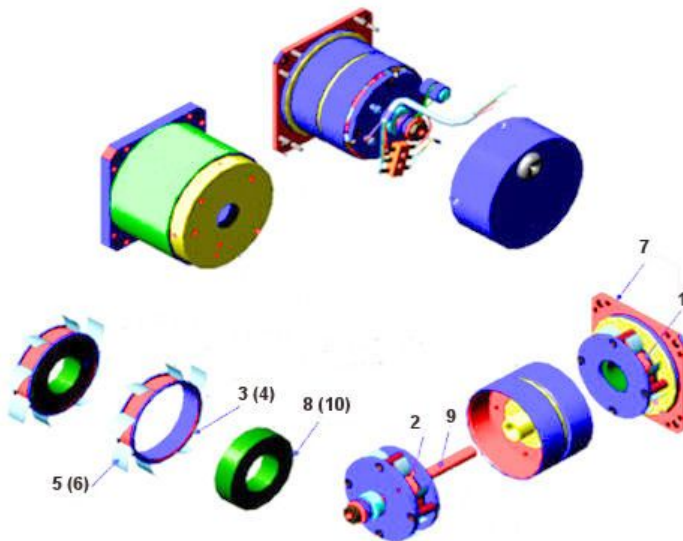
Конструкція п'єзоелектричного двигуна реверсивного обертання
